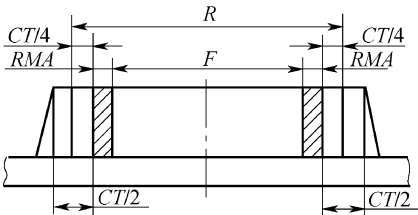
外对称加工表面或双侧加工表面铸件基本尺寸示意图
